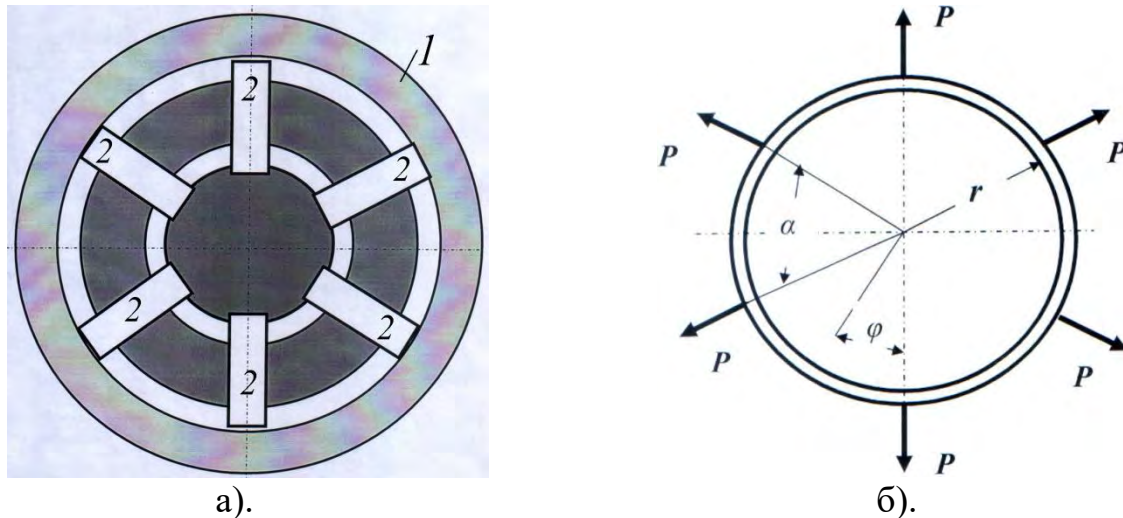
Схемы нагружения кольцевой заготовки 6-ю равномерно распределенными радиальными усилиями: а – схема расположения стабилизируемого изделия и плунжеров, б – схема нагружения кольца радиальными силами
